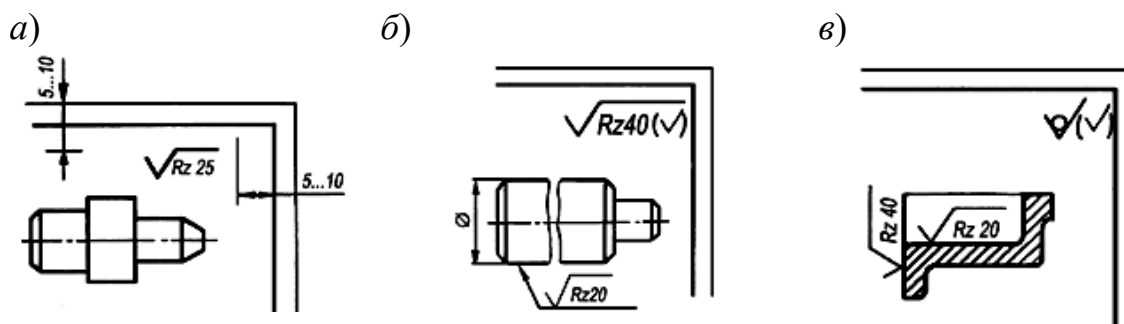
Обозначение одинаковой (а) и преобладающей (б, в) шероховатости
